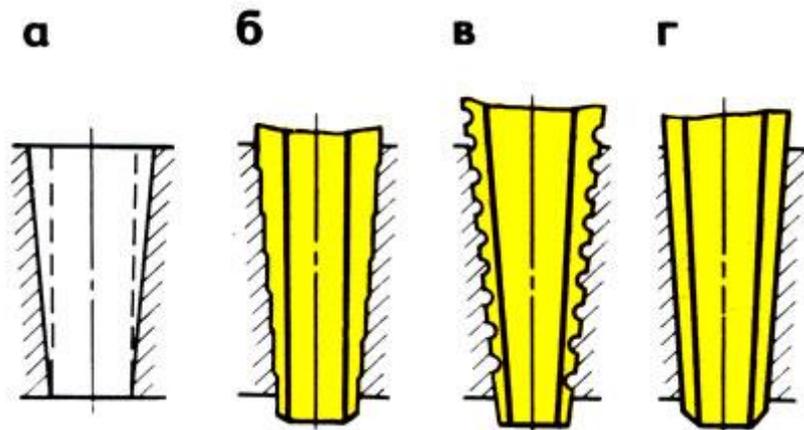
Обработка конических отверстий: а - деталь с коническим отверстием, б - обработка отверстия ступенчатым зенкером, в - развертывание разверткой со стружкопными канавками, г - развертывание конической разверткой с гладкими режущими лезвиями
